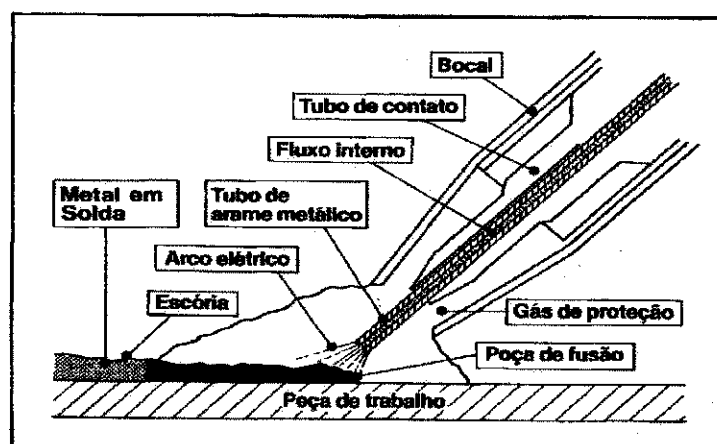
Esquema do Processo de Soldagem Eletrodo /Tubular (Marques, P. V. 1991.)
